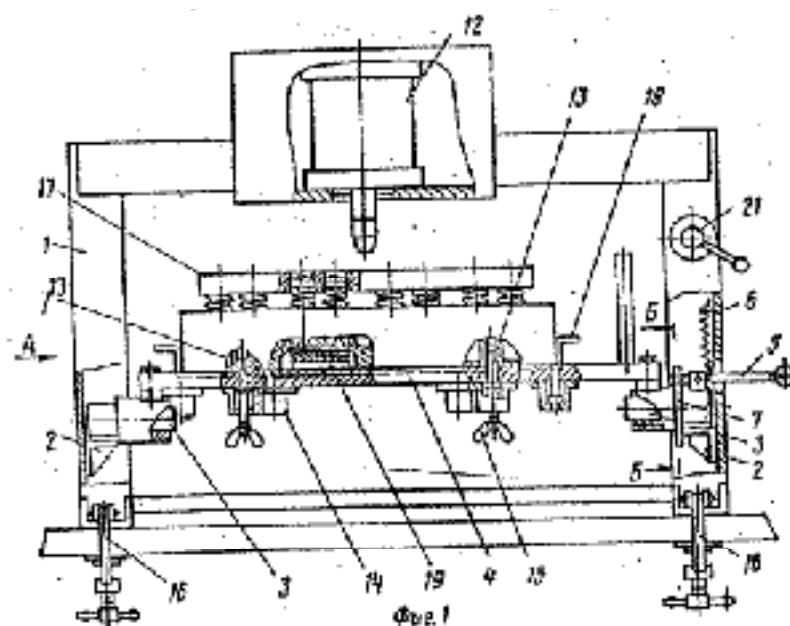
Стенд для разборки и сборки блоков цилиндров двигателей
